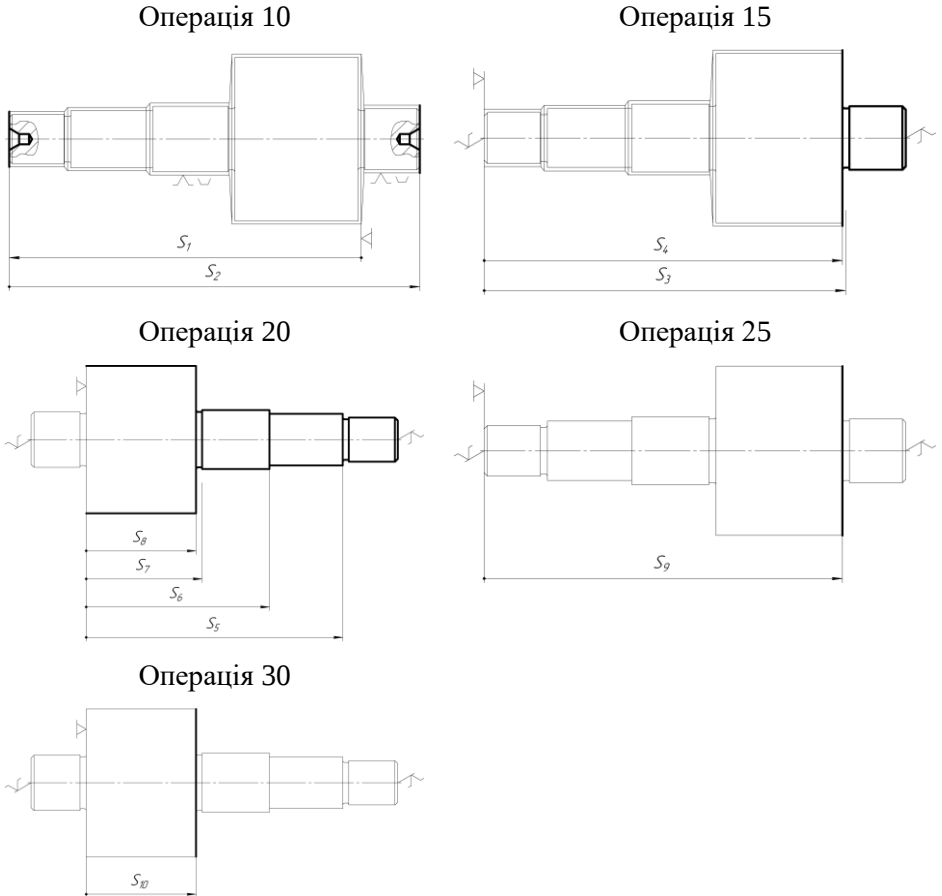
Маршрут виготовлення деталі вал-шестерня
